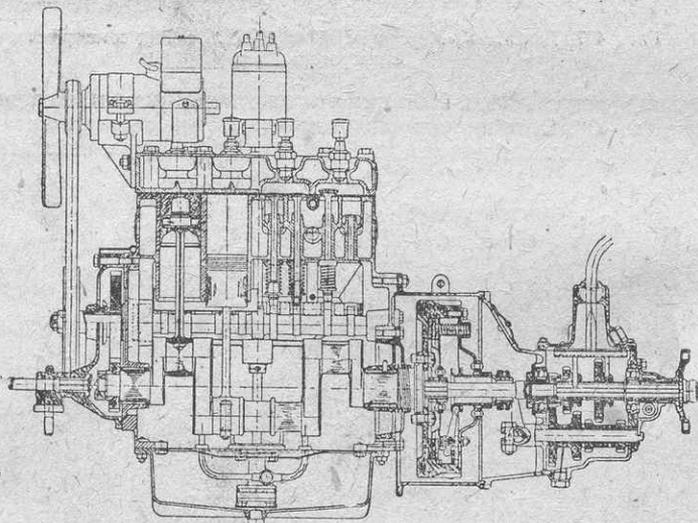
Продольный разрез 16-сильного двигателя «Ханомаг».
